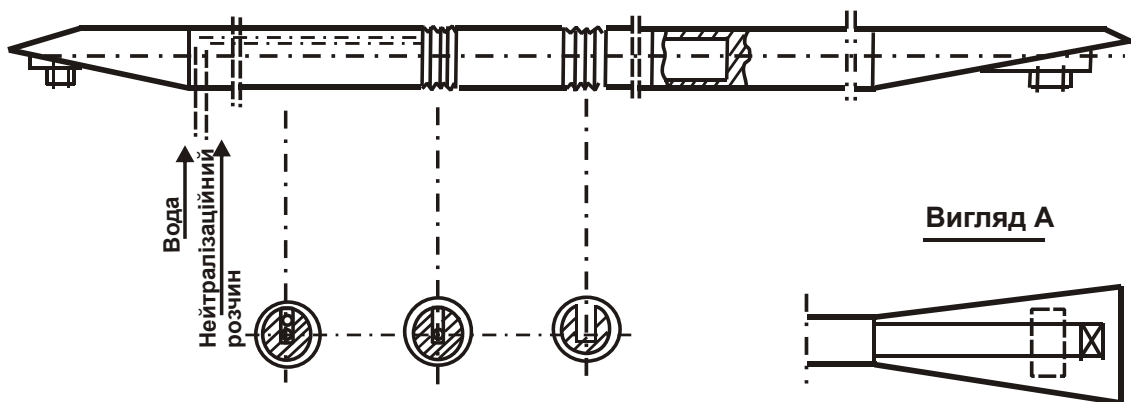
Установа для електрохімічного полірування трубчастої заготовки зі стрічки
